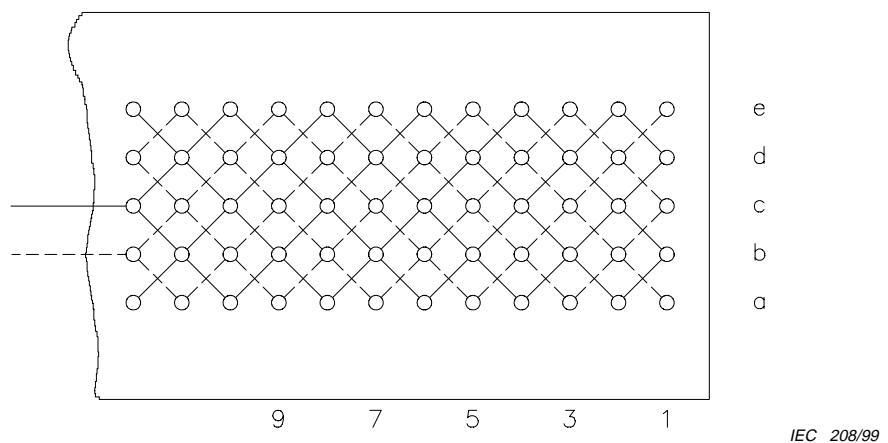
Arrangement pour l'essai d'inflammabilité
